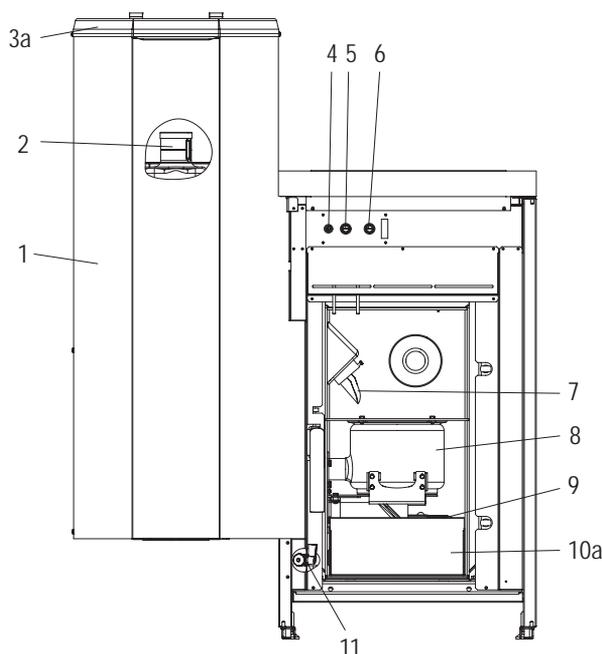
Chaudière à pellets remplissage manuel sans porte de revêtement et sans porte de chambre à combustion
